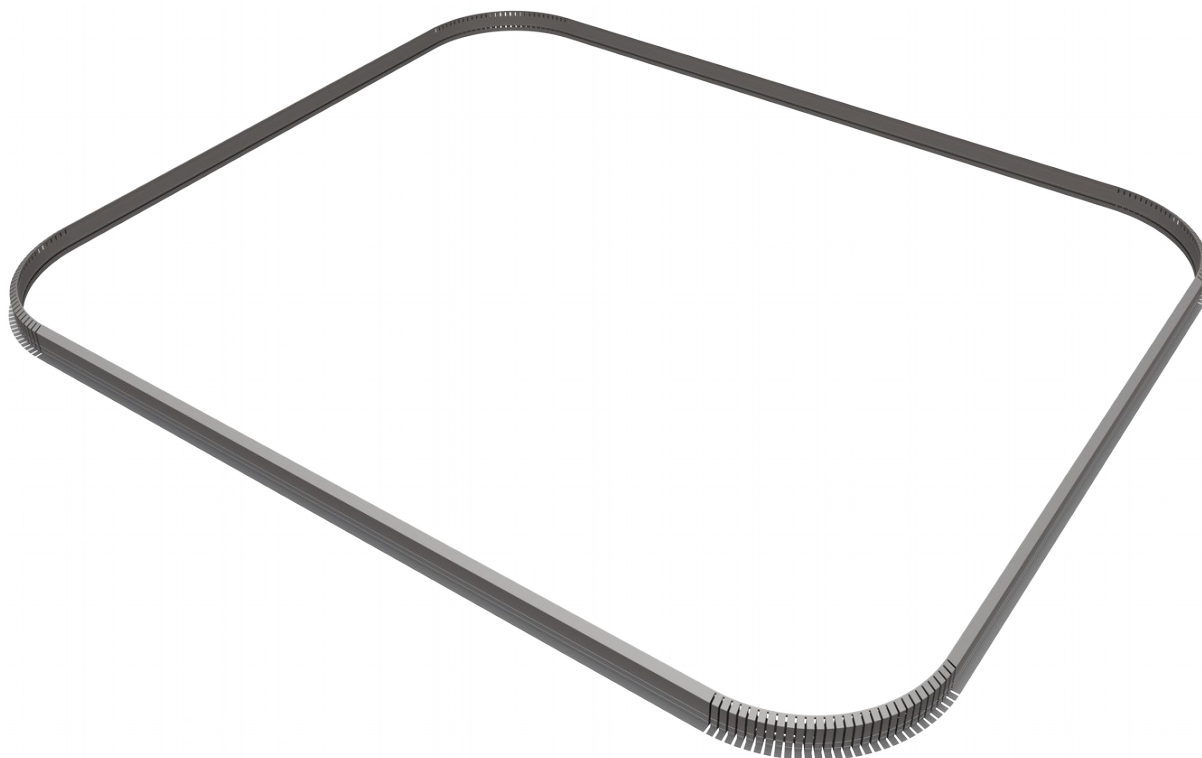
Прямоугольник со скругленными углами. Показанный образец собран из профиля ПП.
